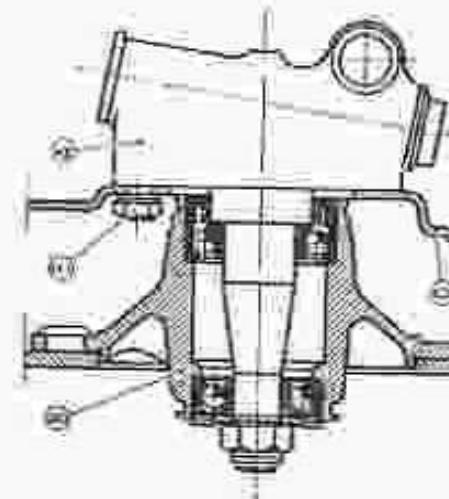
Assemblage de la cuve et du plateau : Première montagne.
